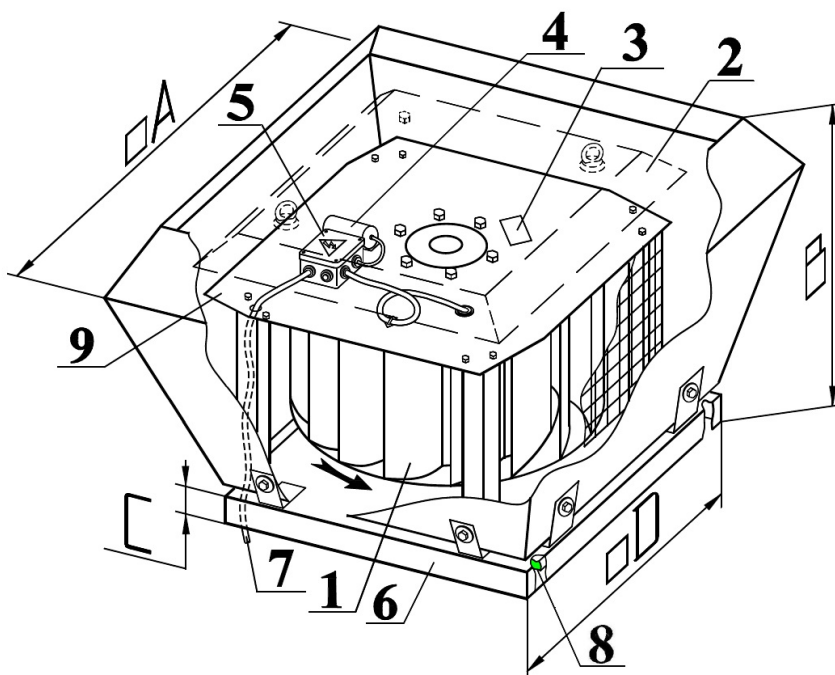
Внешний вид и основные размеры вентиляторов VS 30/22-2E ÷ VS 90/63-6D
